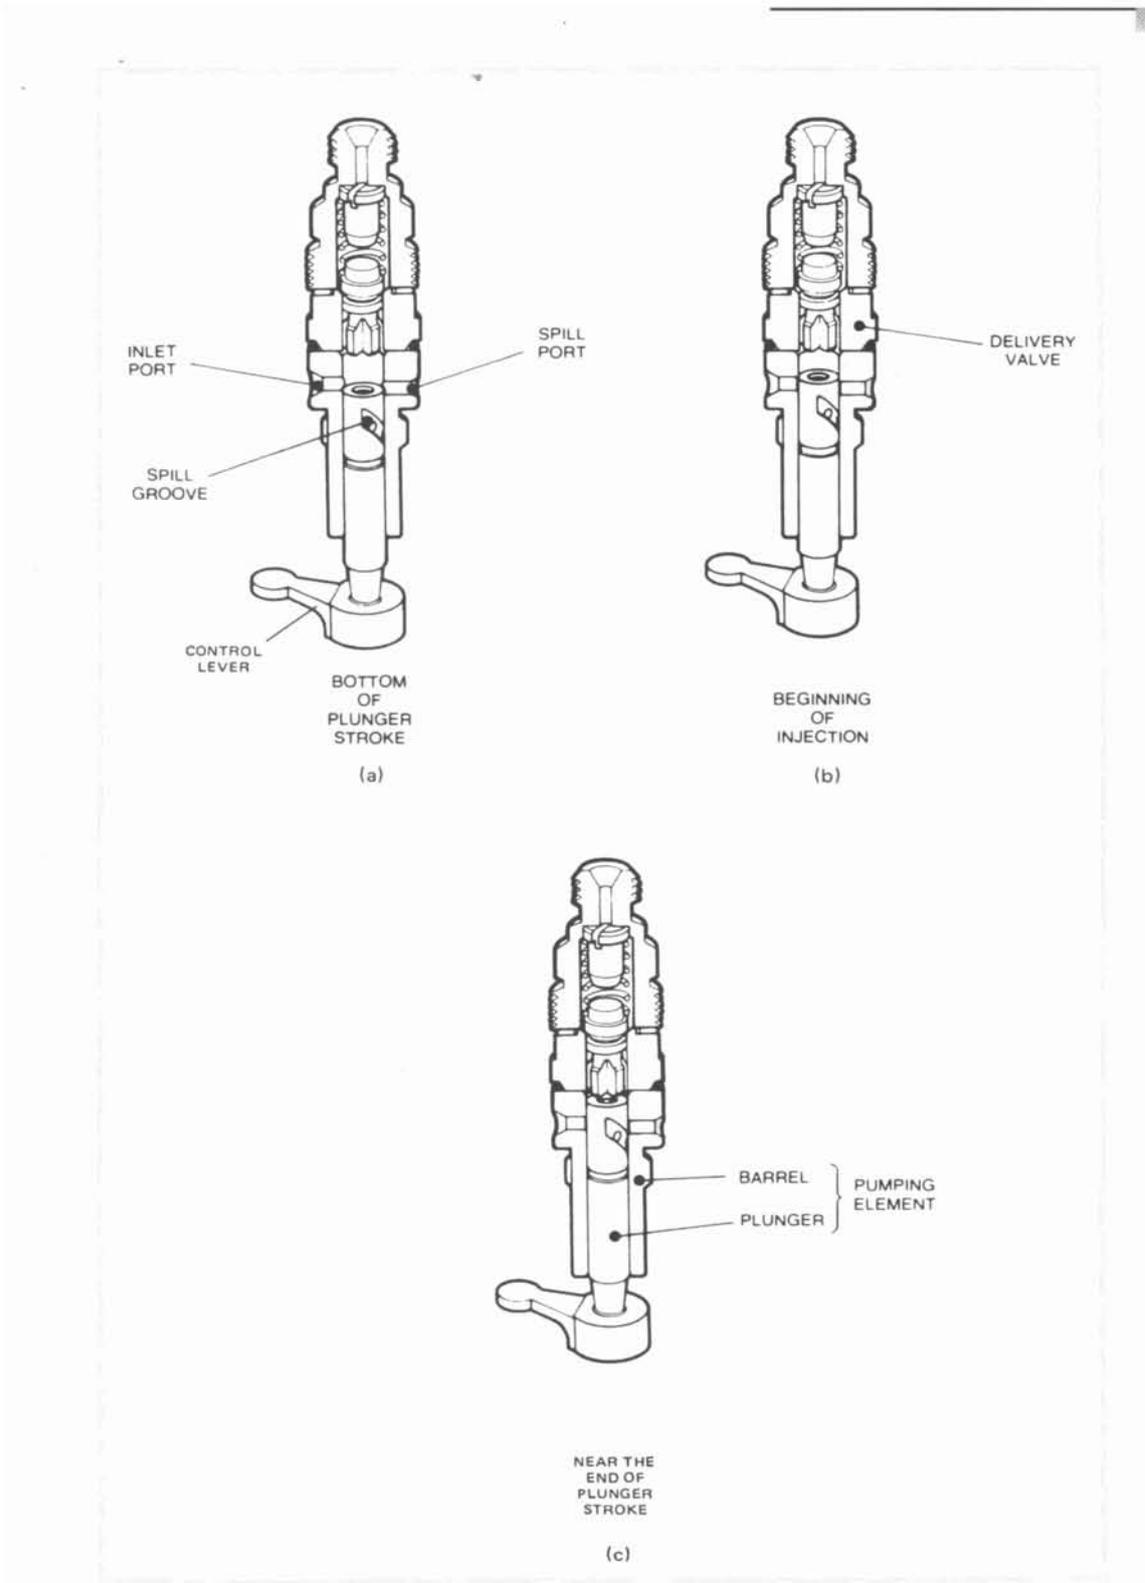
Elementos de Bombeo de Combustible de una bomba en-línea
